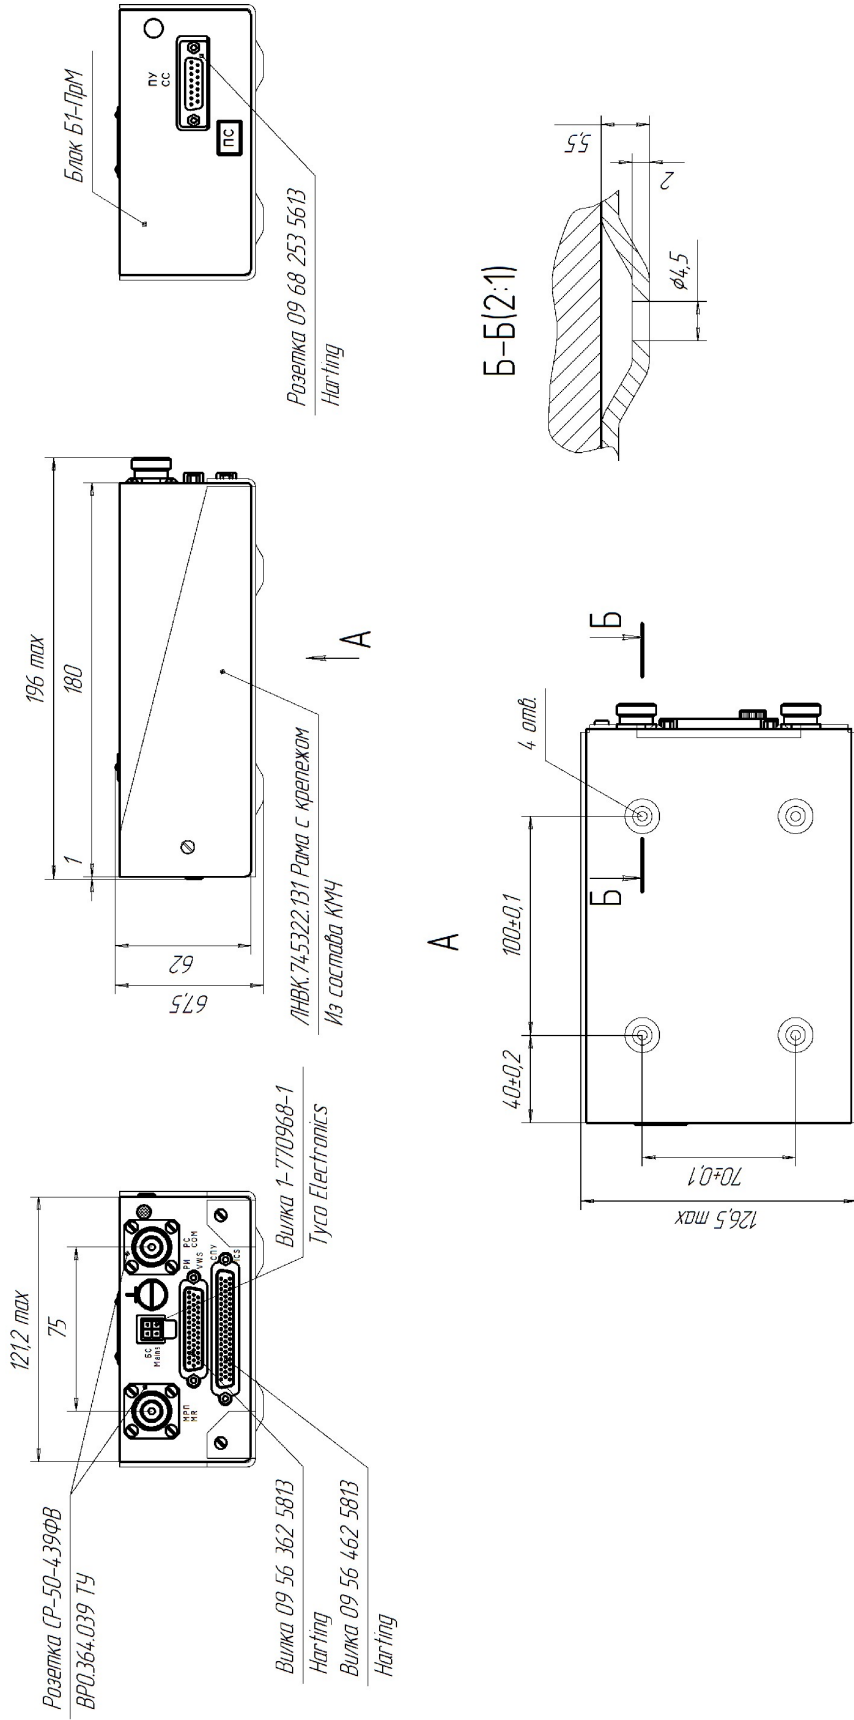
Габаритный чертеж блока Б-1-ПрМ на раме
